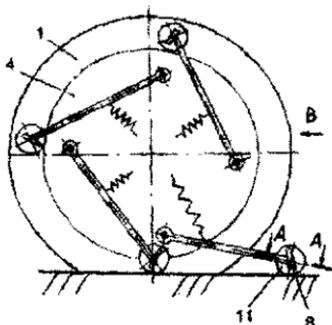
Колесный движитель при движении по дорогам с твердым покрытием с большой деформацией шины, вид сбоку
